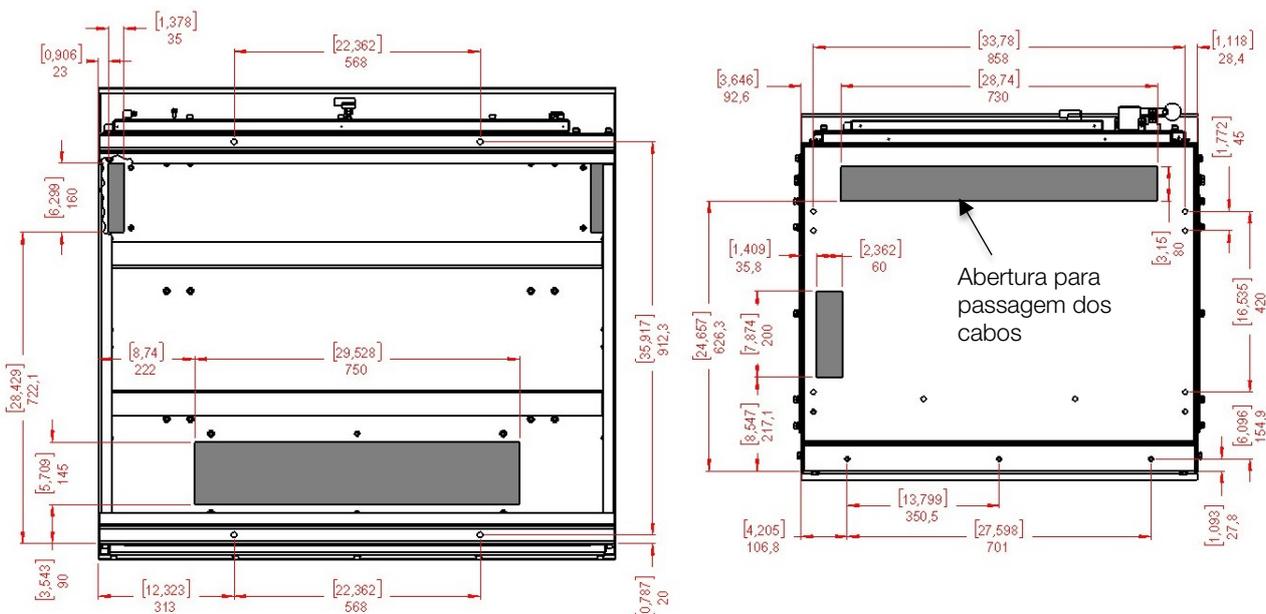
(b): Fixation du panneau SSW7000 au sol (dimensions en mm [pouces]).
